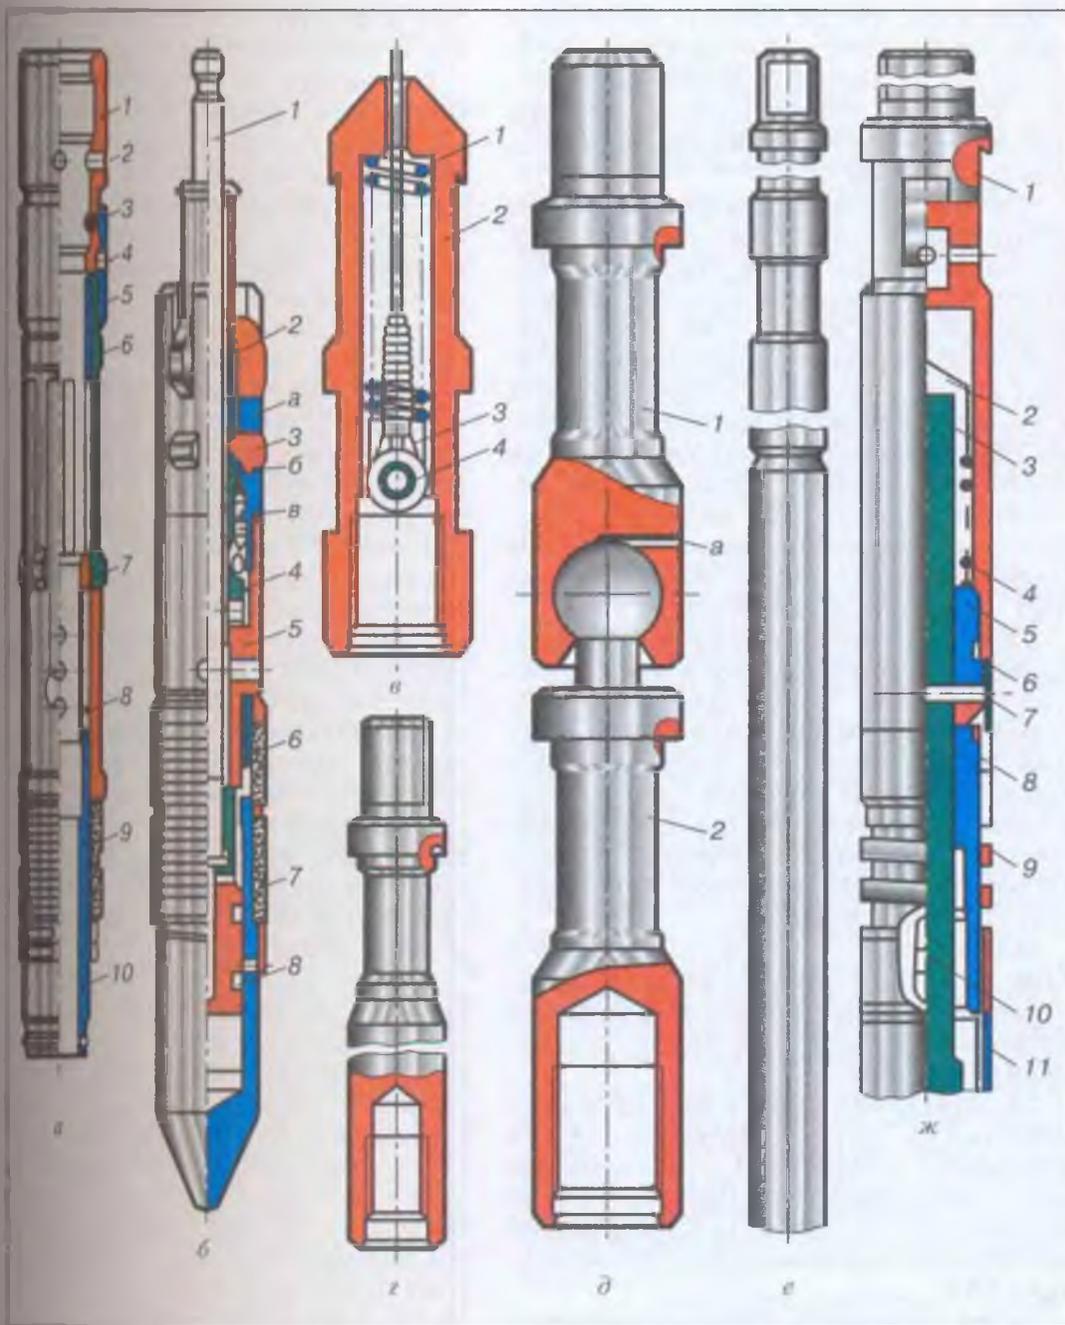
Подземное эксплуатационное оборудование: а – замок (1 – ловильная муфта; 2, 4 – срезной винт; 3 – захват; 5, 7 – втулка; 6 – цапга; 8 – пружина; 9 – уплотнение; 10 – корпус); б – пробка (1 – пистолет; 2 – упор; 3 – захват; 4 – гильза; 5 – корпус; 6 – уплотнение; 7 – поршень; 8 – наконечник; а – канавка; б – выступ гильзы; в – выточка гильзы); в – устройство для закрепления проволоки (1 – пружина; 2 – корпус; 3 – втулка; 4 – ролик); г – грузовая штанга; д – шарнир (1 – головка; 2 – муфта; а – отверстие); е – механический ясс; ж – цапговый инструмент (1 – головка; 2 – колпачок; 3 – сердечник; 4, 9 – пружина; 5 – переводник; 6 – крышка; 7 – штифт; 8 – корпус; 10 – ограничитель; 11 – цапга).
